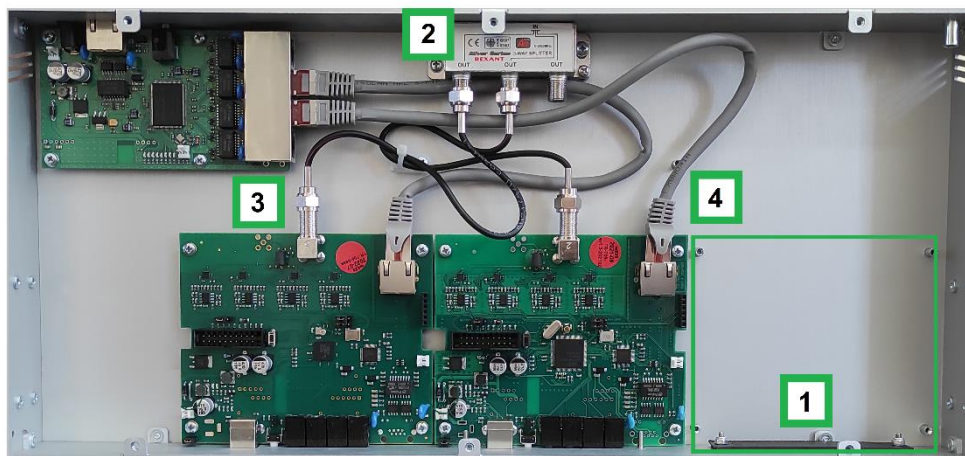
Установка модуля TP-705-0 в rack-корпус
